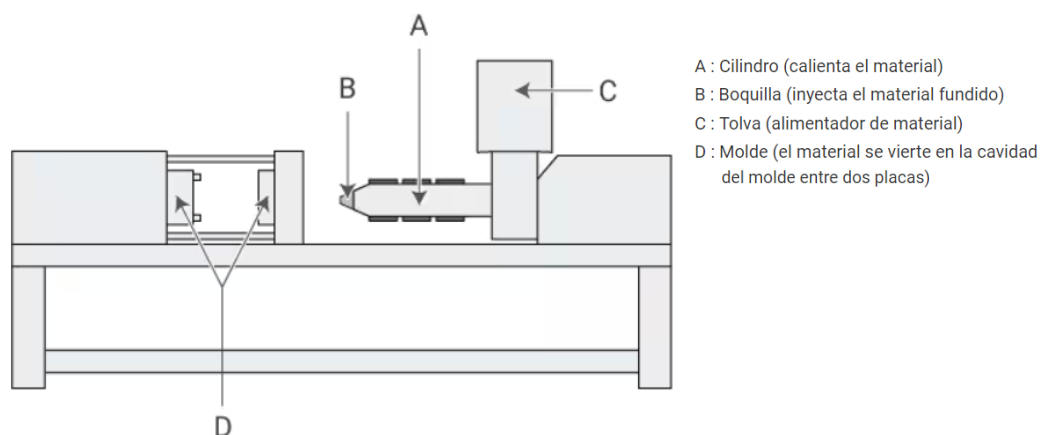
Estructura básica de una máquina inyectora. Tomado de <https://www.keyence.com.mx/ss/products/measure-sys/machining/injection-molding/about.jsp>
